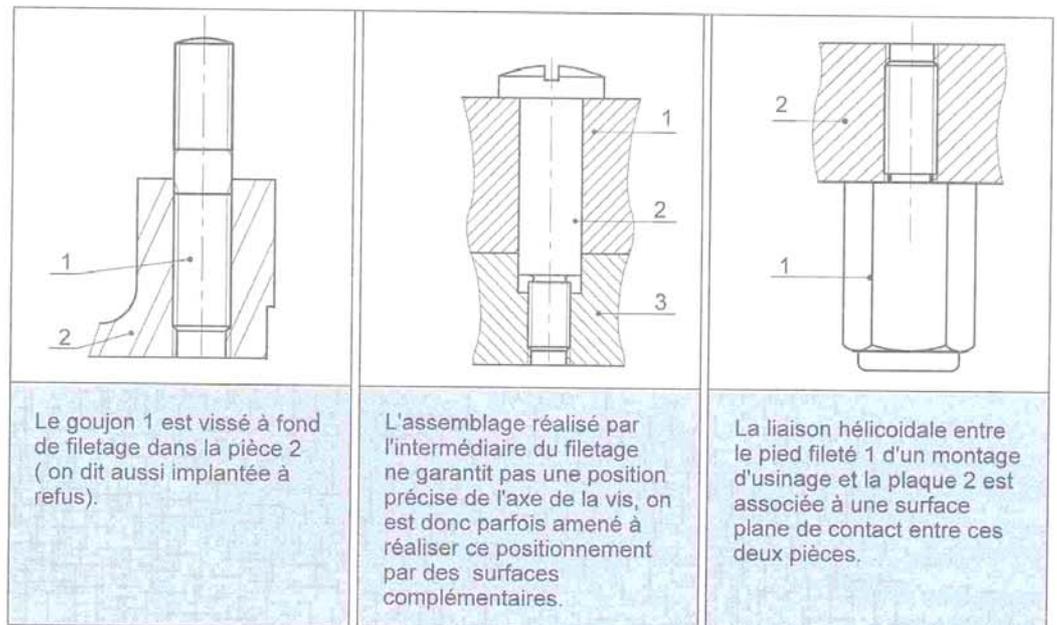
Exemples de solutions constructives réalisant un assemblage démontable par utilisation de surfaces hélicoïdales.
